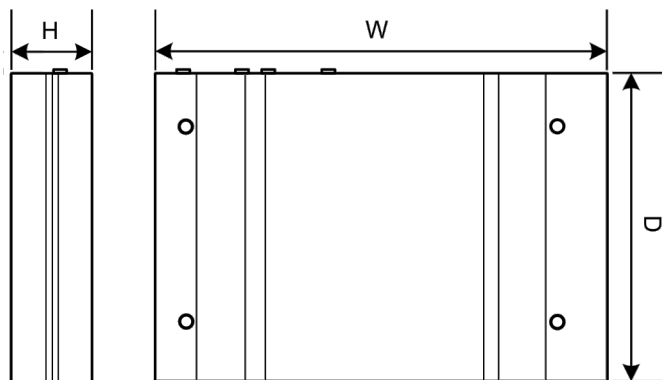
Skematisk fremstilling, dimensioner i millimeter
